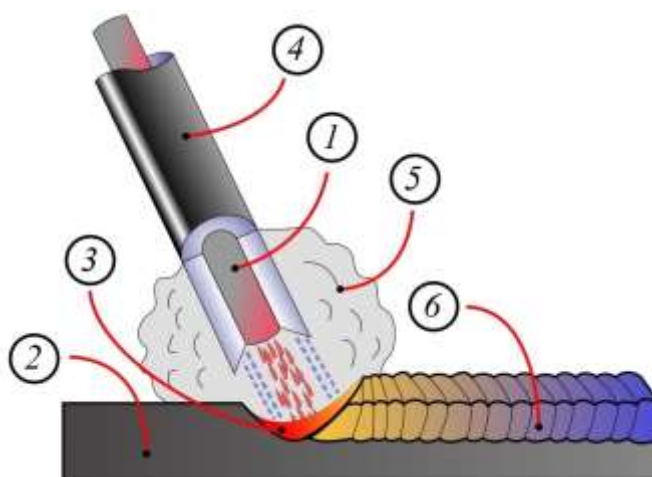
Електродугове зварювання плавким електродом: 1 – електрод; 2 – заготовка; 3 – зварювальна ванна; 4 – електродне покриття; 5 – захисний газ; 6 – шов
